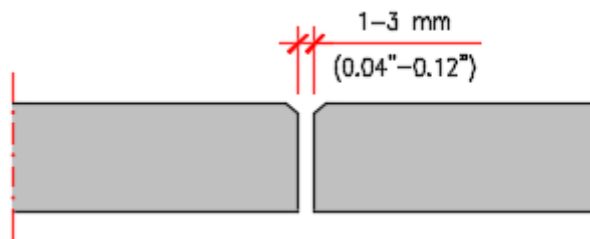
Bearbeitete Kanten mit Fase
